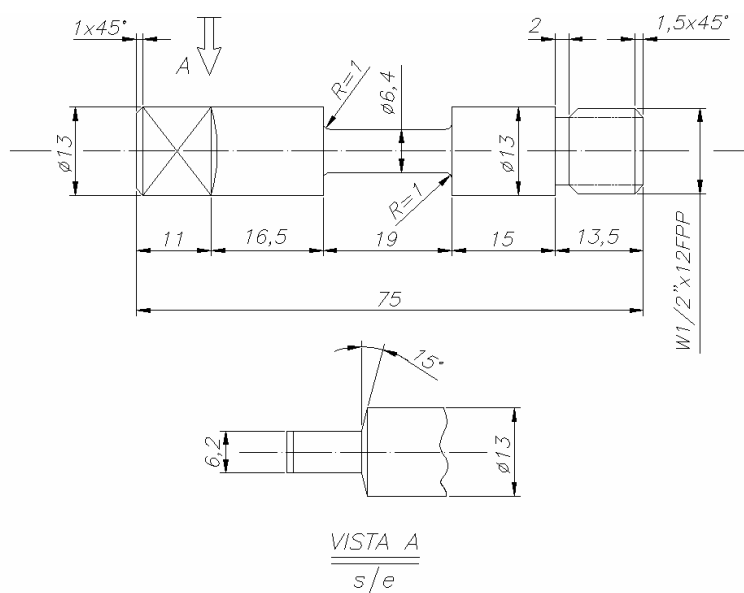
Dimensões (em mm) do corpo de prova do tubo de DIN X20Cr13 para ensaios de torção a quente.
